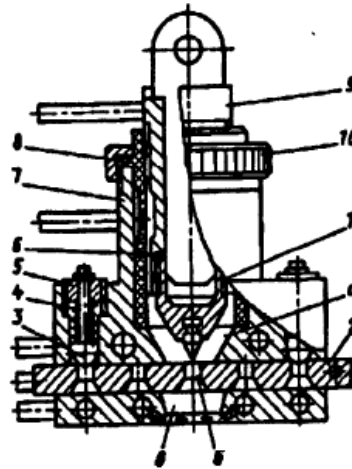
Плазматрон ГСП-1282 ППНМО: 1 – електрод; 2 – сопловий блок; 3 – стопор; 4 – пружина; 5 – втулка; 6 – прокладка; 7 – корпус; 8 – ізолятор; 9 – корпус; 10 – гайка; а – канал; б, в – соплові отвори.
